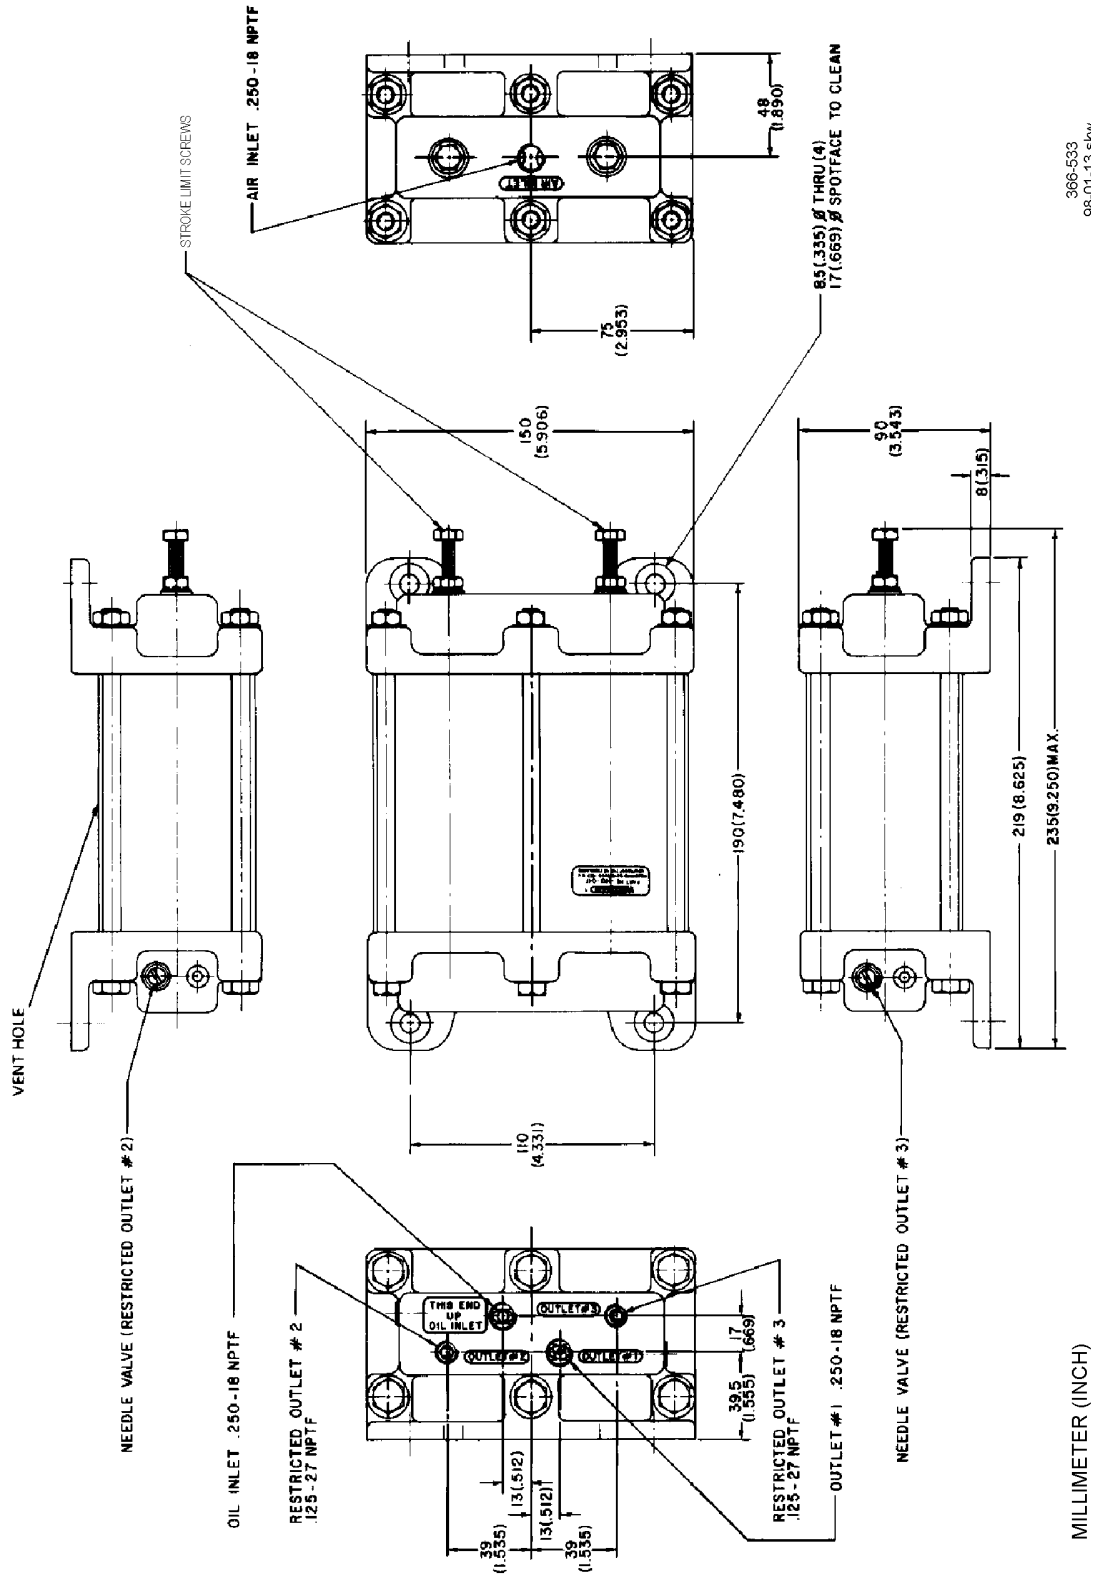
Габаритный чертёж одноцилиндрового бустера
